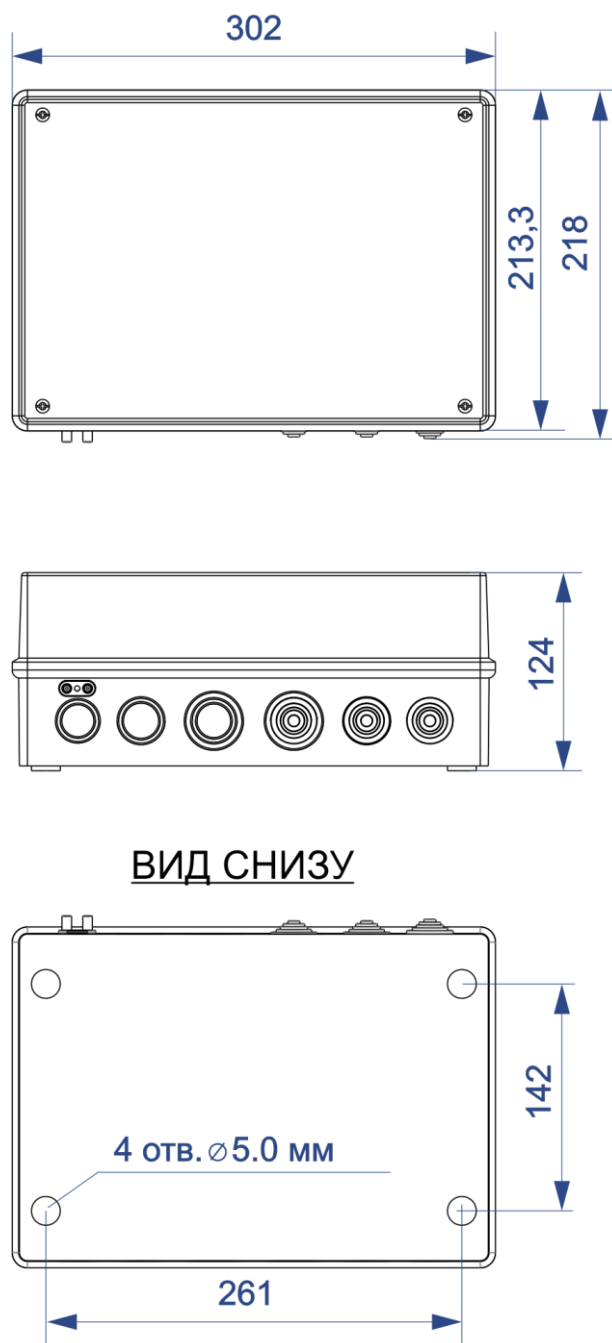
Габаритные и установочные размеры исполнения BOX3
